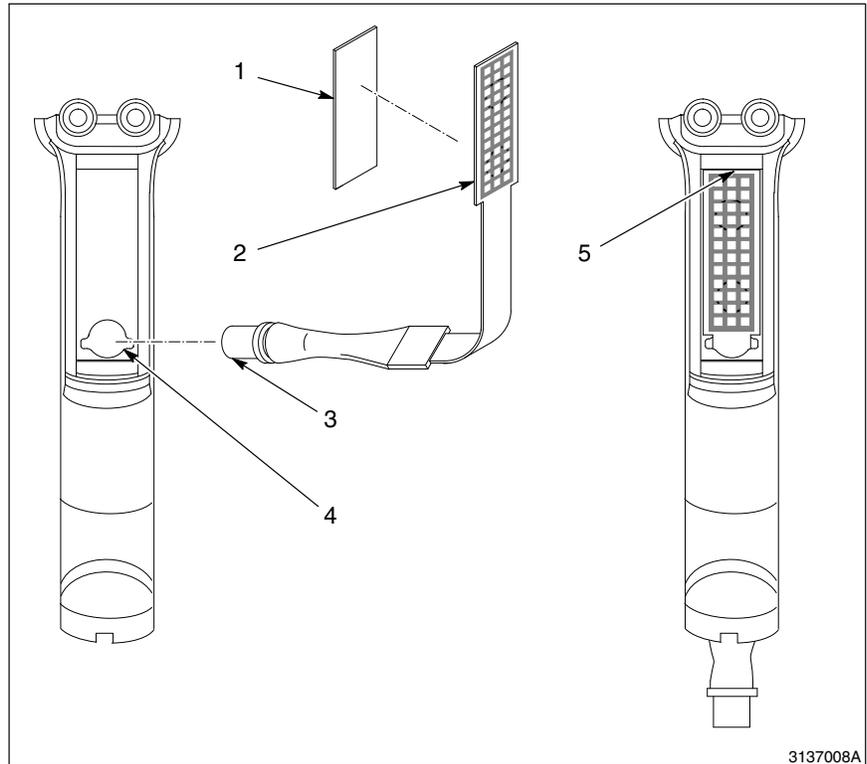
Remplacement du bloc de contact gâchette/purge
